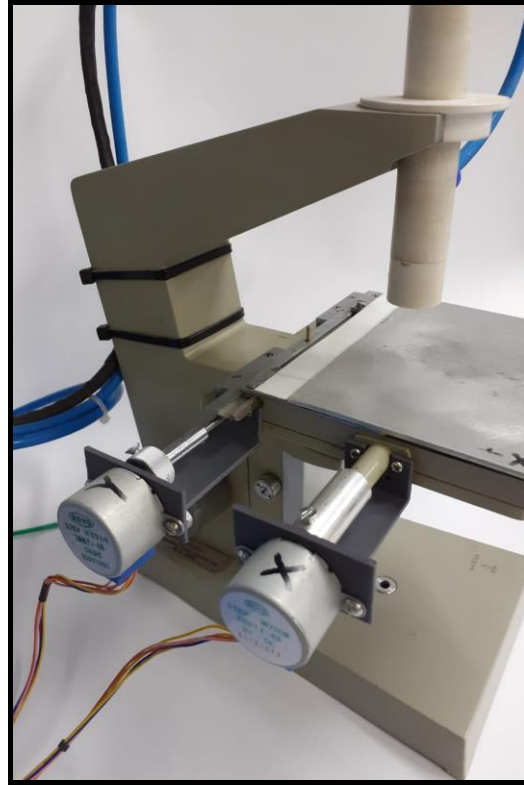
Imagem do suporte do motor de passo do eixo Y fabricado por processo aditivo em impressão 3D.
